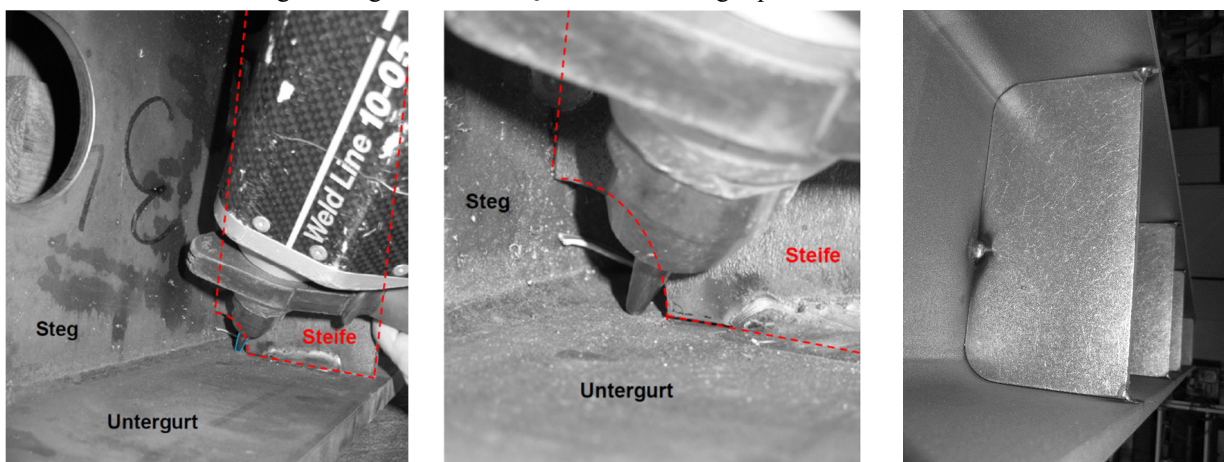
Praxistest mit PIT-Gerät an geschweißtem Träger mit Quersteife und kreisförmigem Freischnitt $r = 30$ mm und rechts Ausführung mit eingepasster Quersteife
